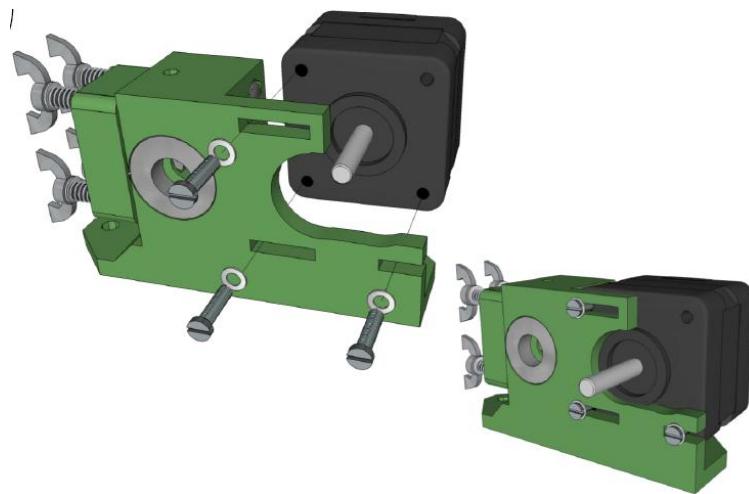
Colocación Montaje del motor y ensamblado de los engranajes (paso 2)
